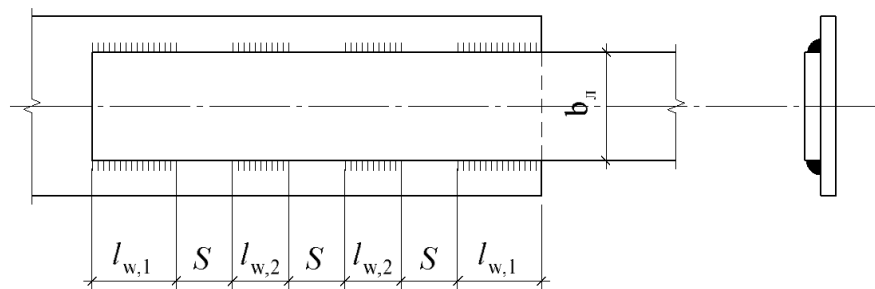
Схема сварного соединения внахлест двух листов прерывистыми швами, расположенными параллельно плоскости листов:
